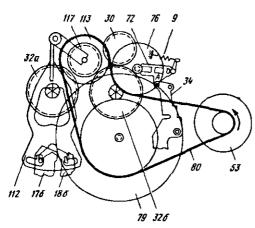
Кинематическая схема ЛПМ 9 — пружива муфты сцепления, 176 — толкательная пластинка обратной перемотки, 186 — толкательная пластинка прямой перемотки, 30 — колесо передаточное промежуточное, 32а — подающий шпиндель, 326 — приемный шпиндель, 34 — подающий шпиндель, 35 — двитатель, 72 — рычаг муфты сцепления, 76 — диск муфты сцепления блока воспроизведения, 79 — маховик, 80 — нассяк, 112 — рычаг быстродействующей муфты сцепления, 113 — быстроходная муфта сцепления, 117 — зубчатое колесо быстроходной муфты сцепления,
